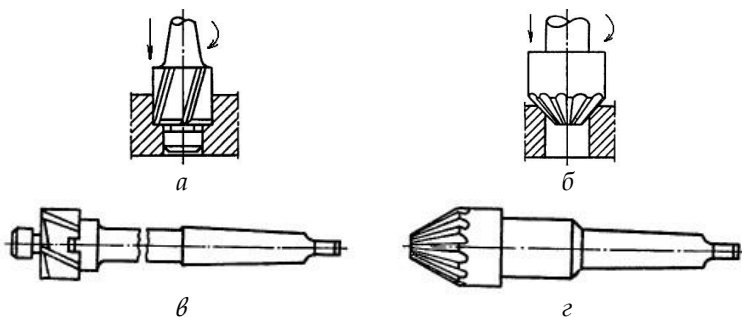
Схема зенкования цилиндрического (а) и конического (б) углубления, цилиндрическая (в) и коническая (г) зенковка
